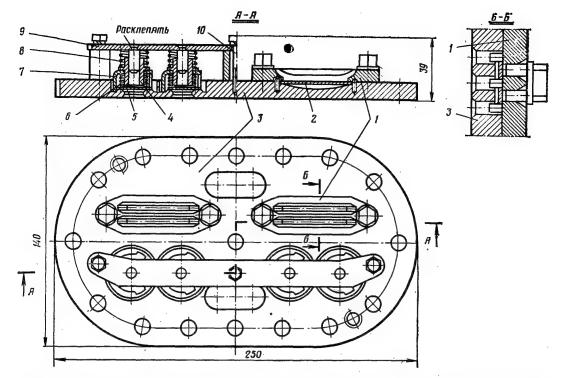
Клапанная плита на двухцилиндровый блок непрямоточного компрессора со всасывающими полосовыми и нагнетательными пятачковыми клапанами:
